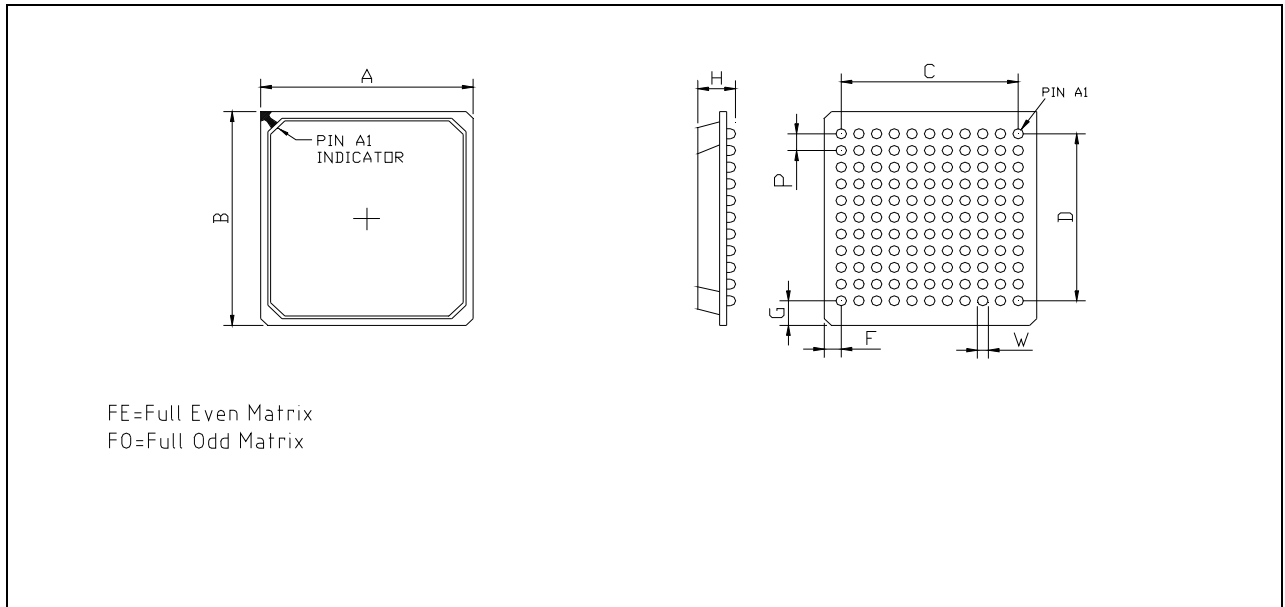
1.27mm PBGA 元件的焊盘尺寸
